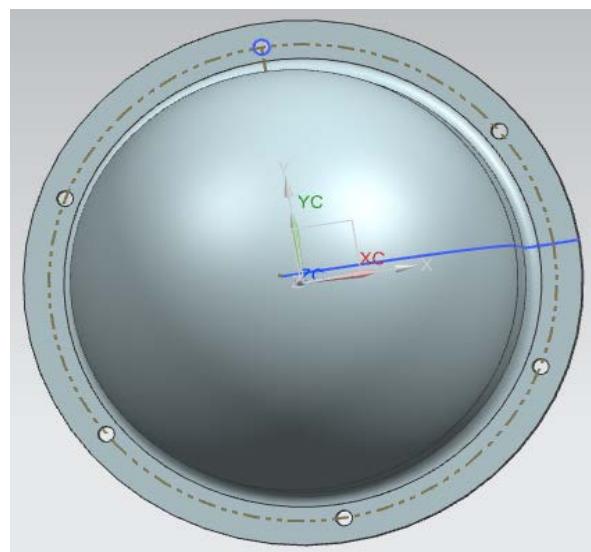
3D модель корпуса с построенными отверстиями
